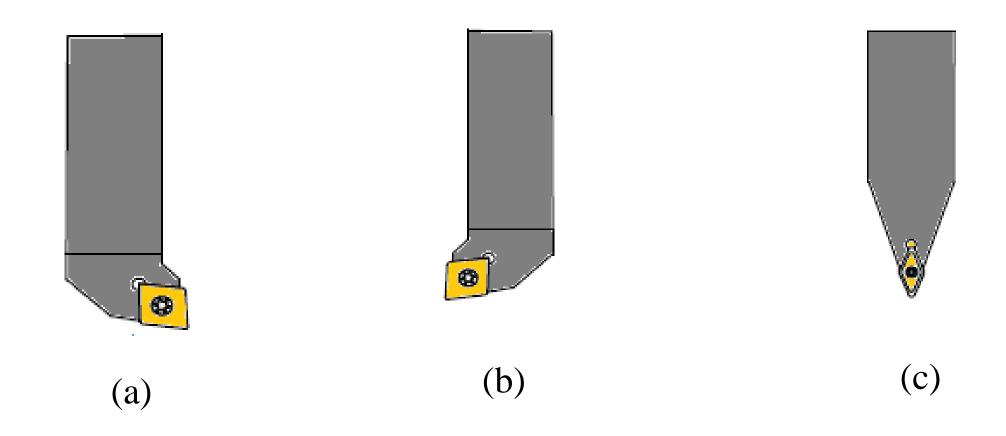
(a) Outil à plaquette en carbure droit R ; (b) Outil à plaquette en carbure gauche L ; (c) Outil à plaquette en carbure neutre.
